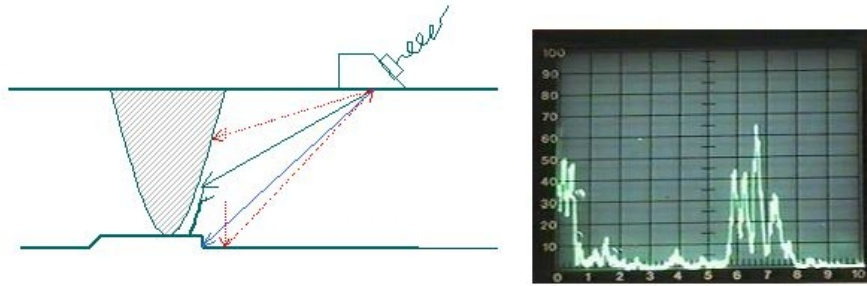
Ultrasonic testing from welded joints. (a) geometry of testing, (b) ultrasonic A-scan signal
